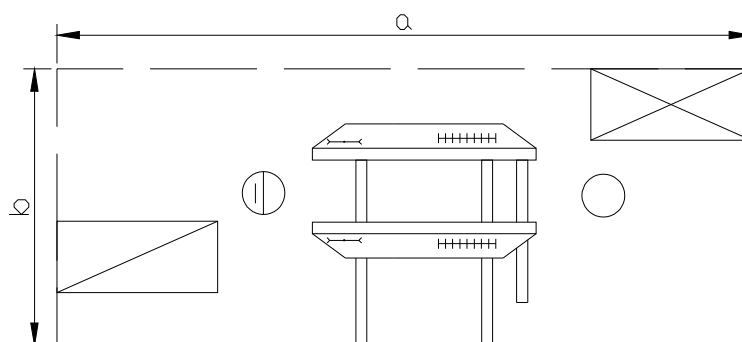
Схема организации рабочего места у двустороннего ящичного шипорезного станка для резки прямых шипов:
